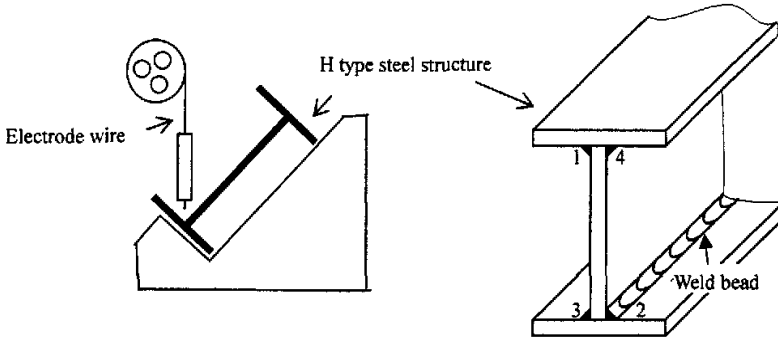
H 型钢的振动焊接及焊缝顺序
